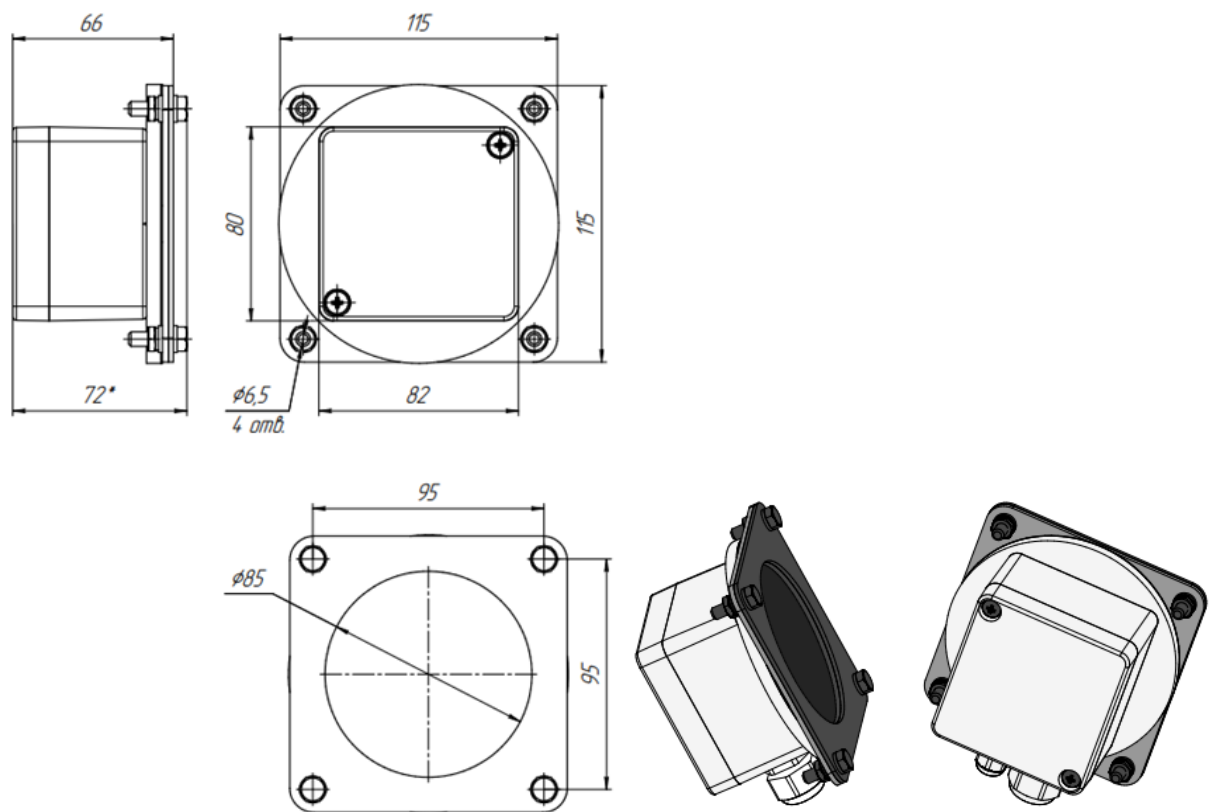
Габаритные и присоединительные размеры ДЗ исп.01
